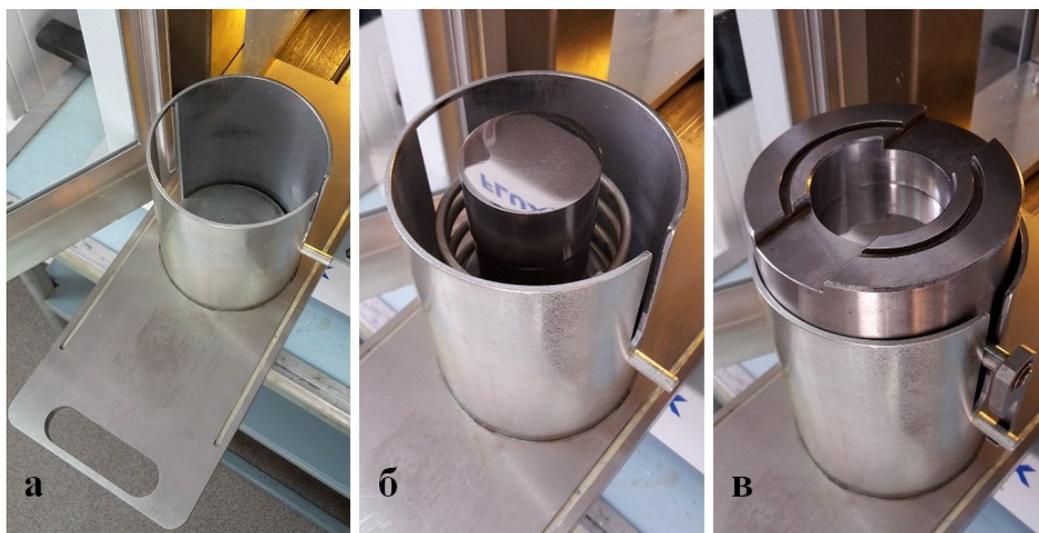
Сборка пресс-формы: а) извлечение подвижной платформы, б) установка основания пресс-формы и пружины, в) установка ячейки пресс-формы в держатель
